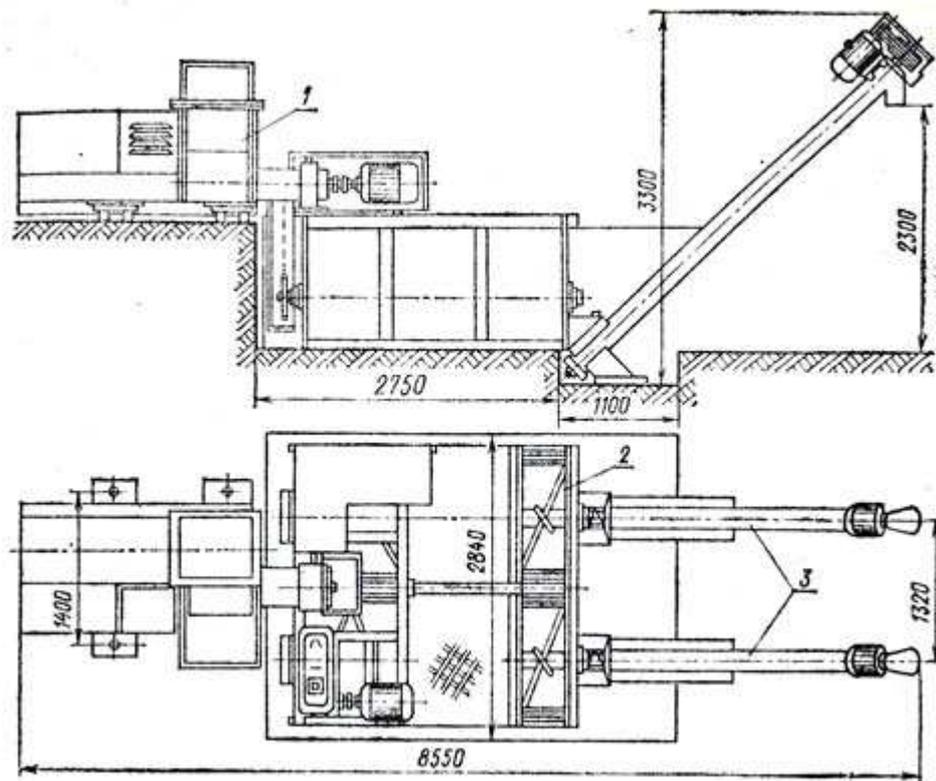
Кормоприготовительный агрегат КПА-69: 1 - измельчитель; 2 - фаршемешалка; 3 - винтовые конвейеры
